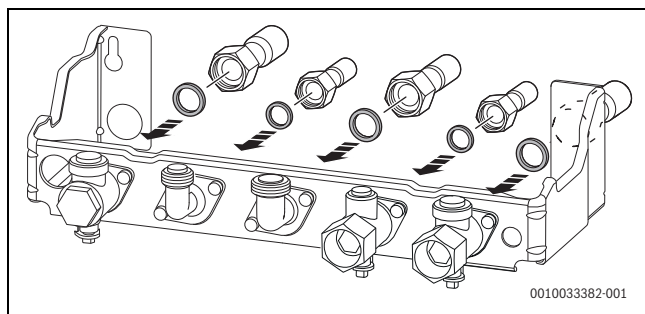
Montar los tubos con las juntas en la plantilla de montaje
